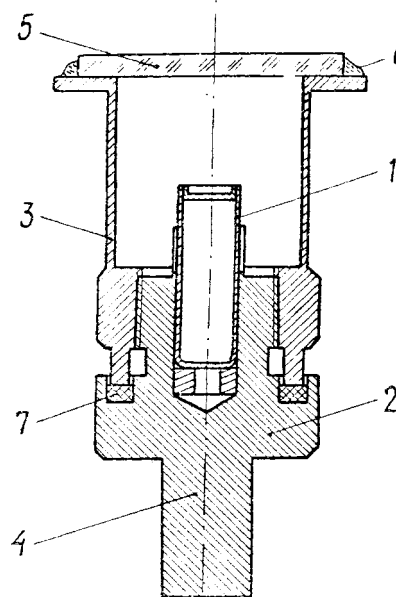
Камера для герметизации тигля лазерной сваркой. 1-тигель с крышкой, 2- основание сварочной камеры, 3- колпак камеры, 4- хвостовик, 5- окно для лазерного луча, 6- экспондная смола, 7- прокладка фторопластовая
